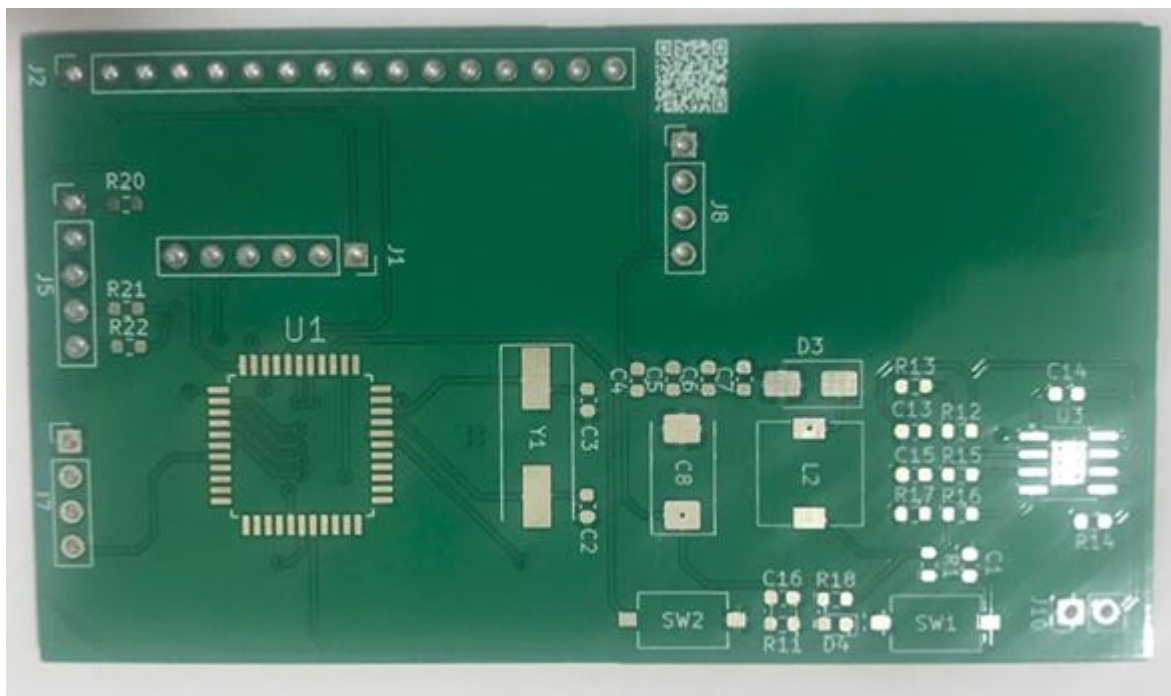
a: *Layout Mạch dán PCB được thiết kế bằng ứng dụng Kicad.
